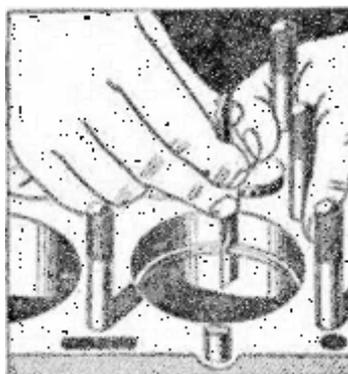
Проверка зазора в стыке поршневого кольца.
